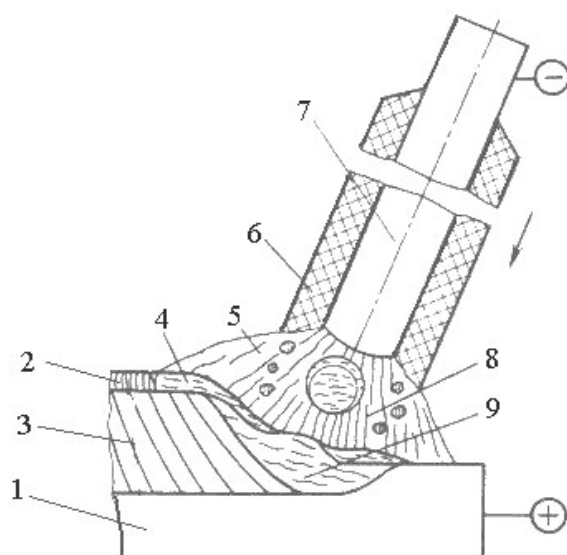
Схема процесса сварки металлическим покрытым электродом:
